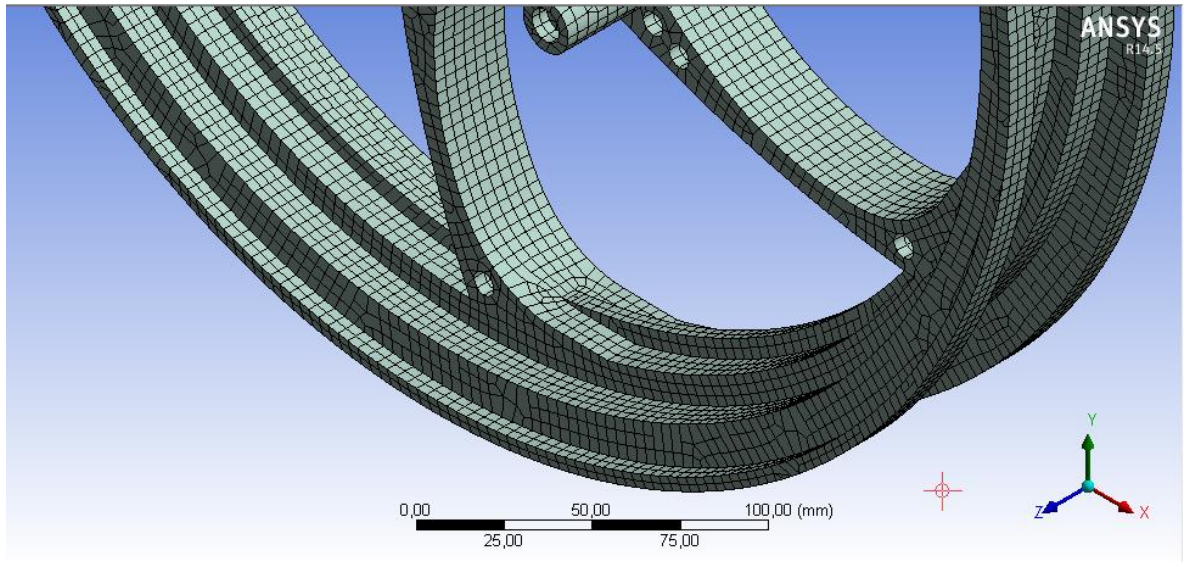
Mallado de elementos de 4 mm del diseño optimizado “a.4”. Fuente: Propia
